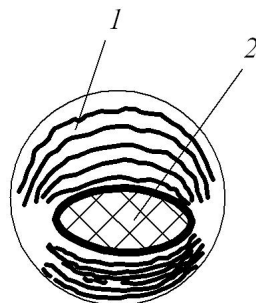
Усталостный излом: 1 – следы фронта трещины; 2 – излом
